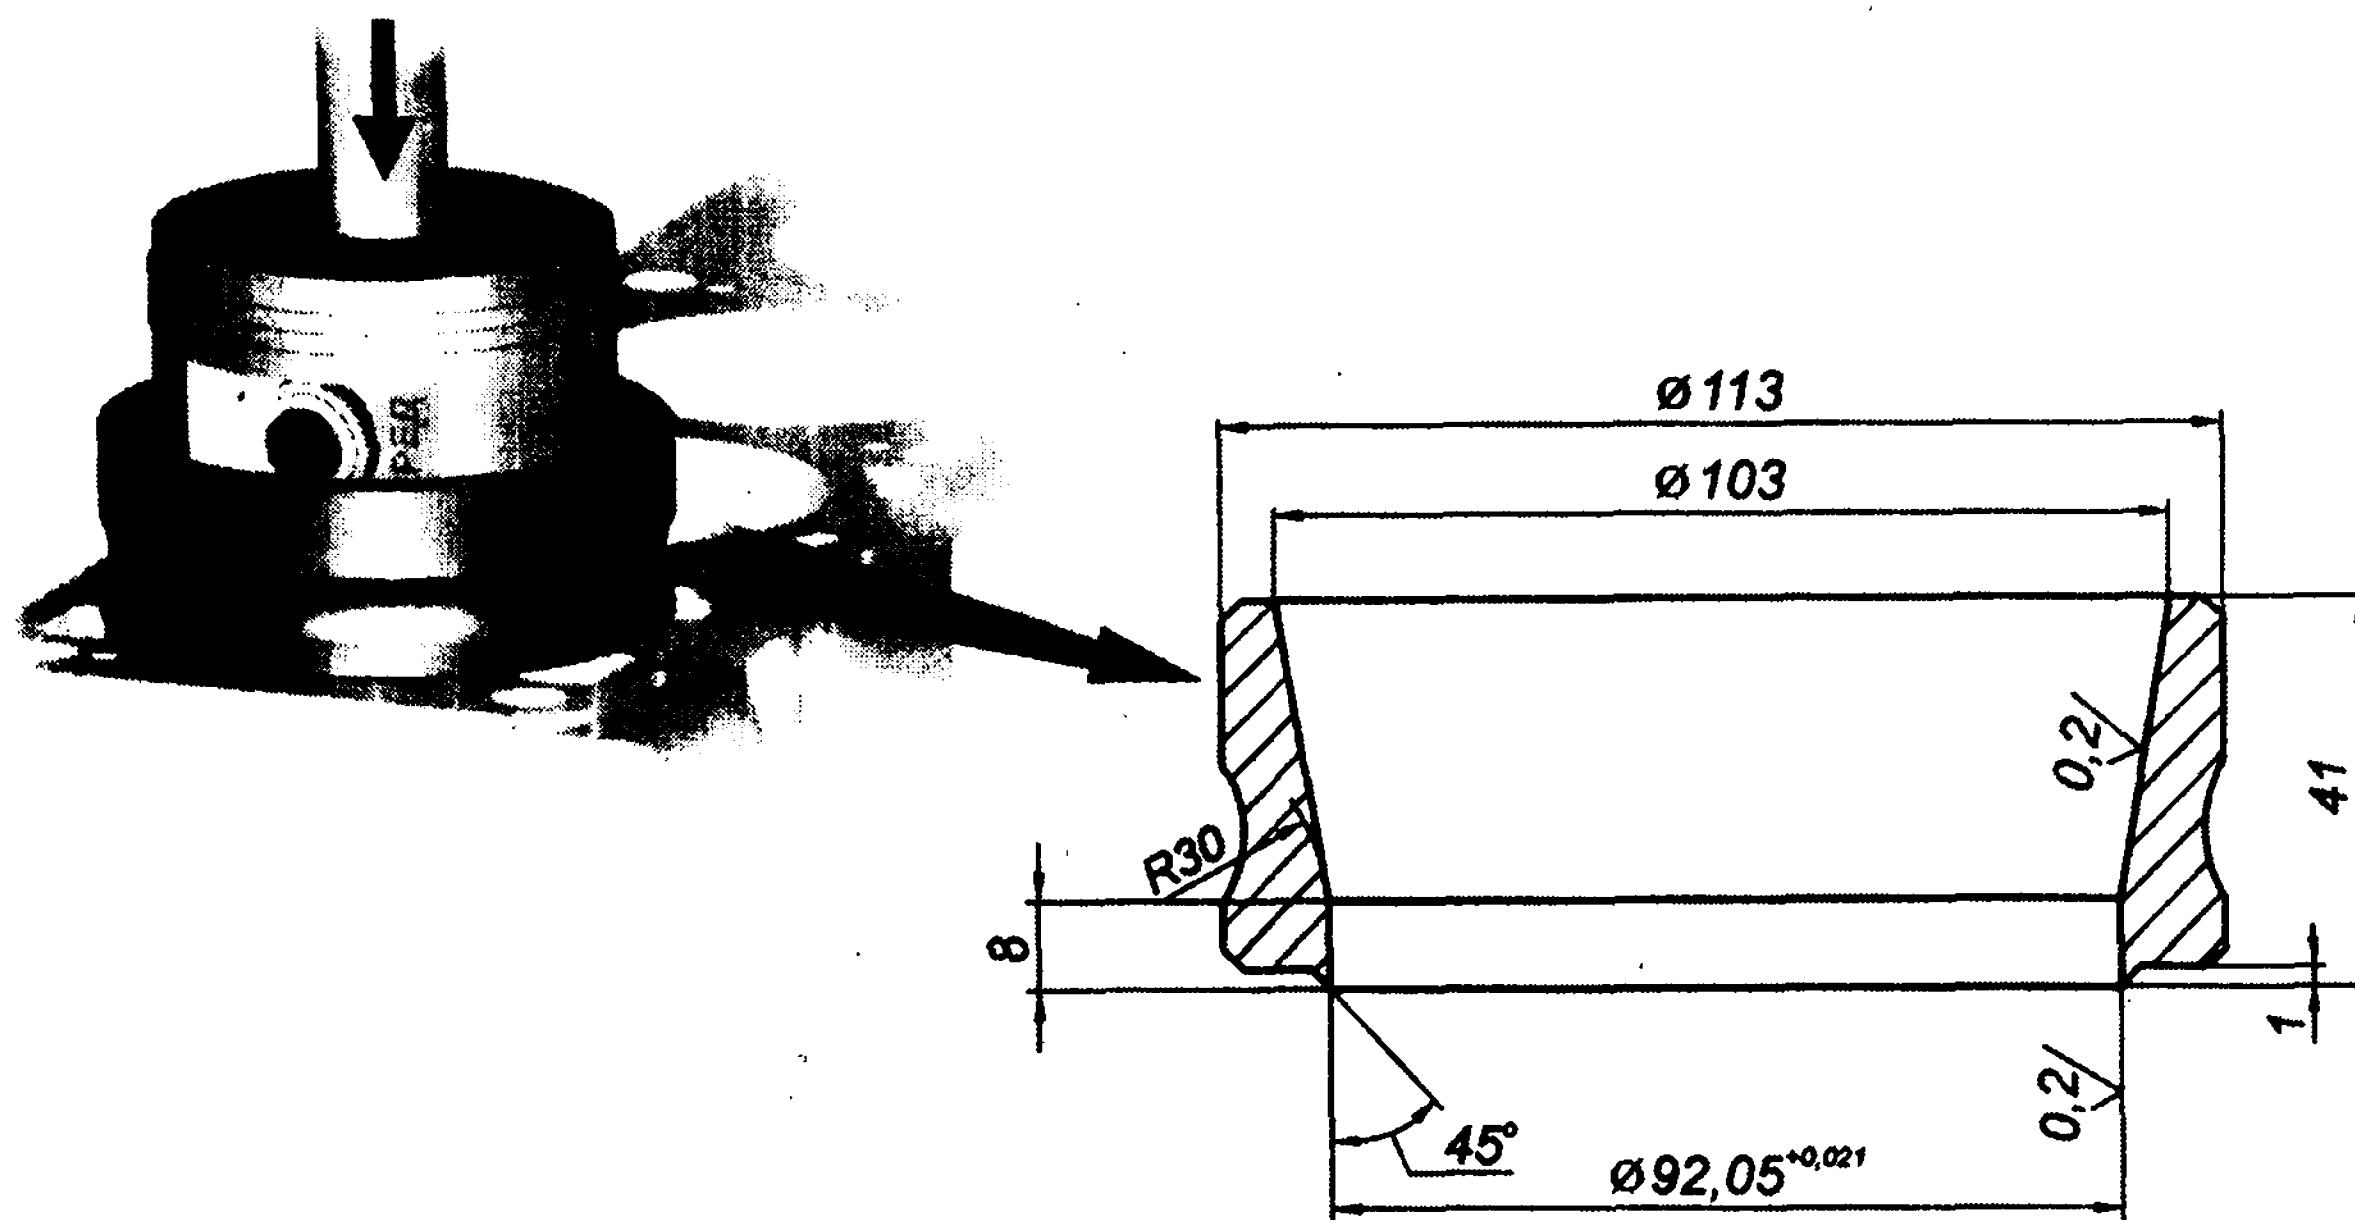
Установка поршня с кольцами в цилиндр с помощью оправки
